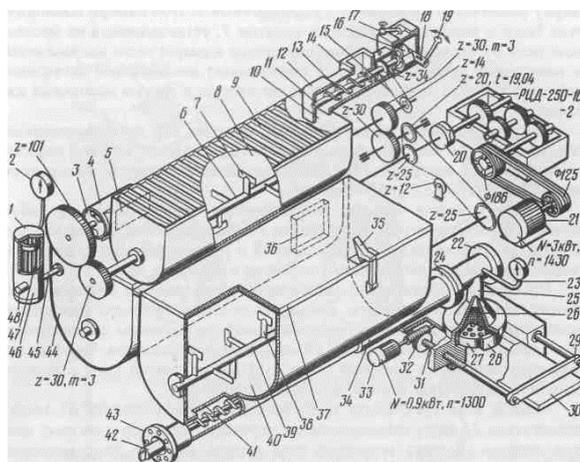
Схема макаронного прессы Б6-ЛПШ-500: 1 - фильтр; 2 - вакуумметр; 3 - роторный питатель; 4 - вакуумный затвор; 5 - окно; 6, 39 - валы месильные; 7, 38 — месильные лопатки; 8, 40, 44 - месильные камеры; 9 - крышка; 10 - отверстие в корпусе дозатора; 11 - полый вал; 12 - корпус дозатора; 13, 42 - шнеки; 14 - приемный патрубок; 15 - цепная передача; 16 - крыльчатка; 17 - вентиль; 18 - прорезь; 19 - рукоятка; 20 - муфта кулачковая; 21, 33 - электродвигатели; 22 - пробка; 23 - манометр; 24, 43 - фланцы; 25 - прессующая головка; 26 - предохранительная сетка; 27 - матрица; 28 - кольцо; 29 - траверса; 30 - направляющая; 31 - винт; 32 - червячный редуктор; 34 - охлаждающая рубашка; 35 - зажимы; 36, 41 - окна; 37 - крышка из органического стекла; 45, 48 - патрубки; 46 - корпус фильтра; 47 - фильтрующая поверхность
